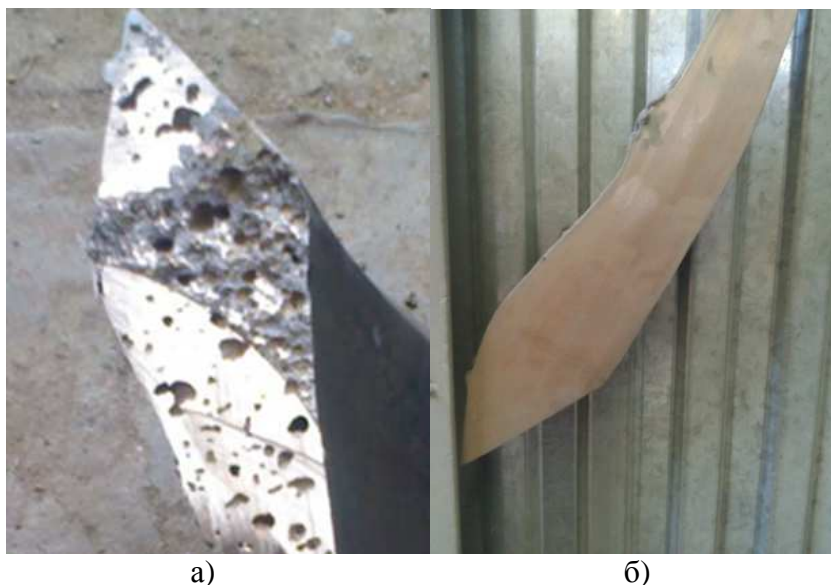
а) Разрез колокола с «медвежьим» звоном («губчатый» разрез), б) Разрез колокола с хорошо сваренным металлом (соблюдение правил металлургии)
